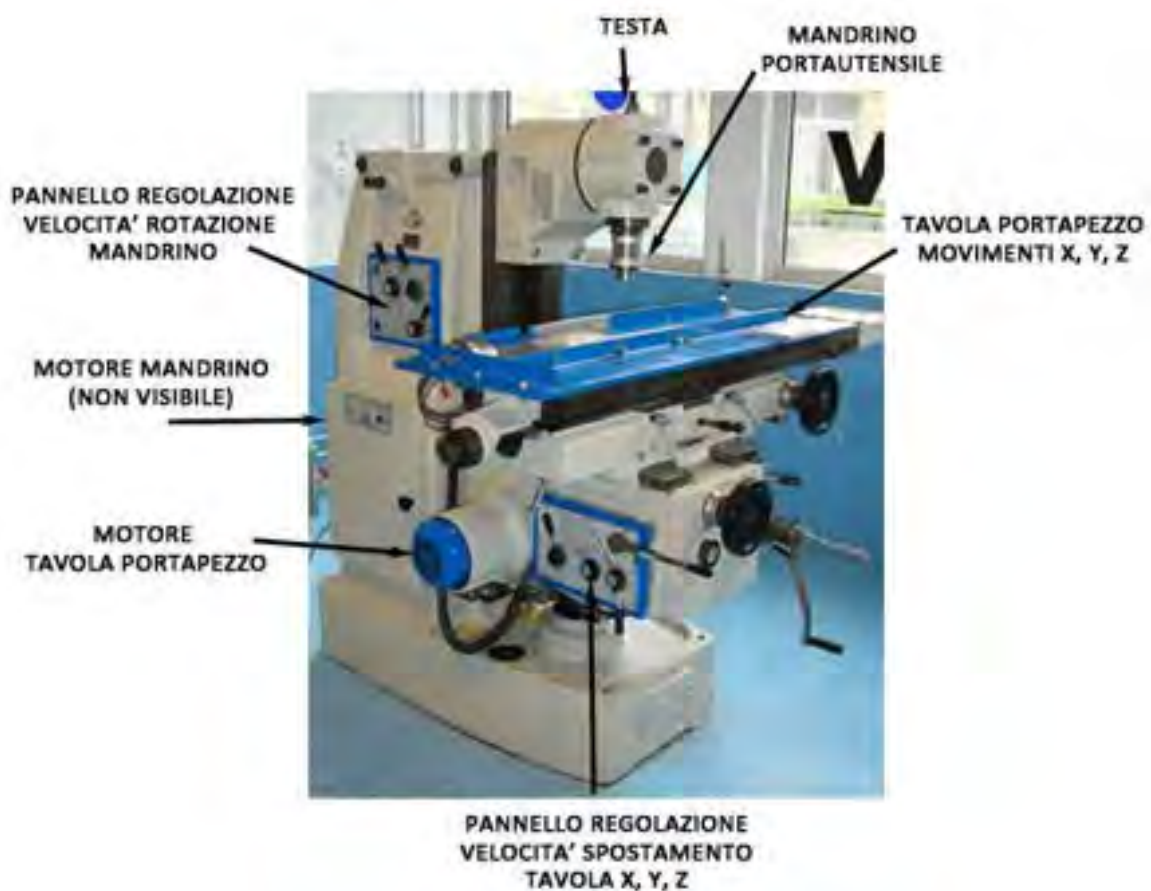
Fresatrice universale trasformata in saldatrice FSW
